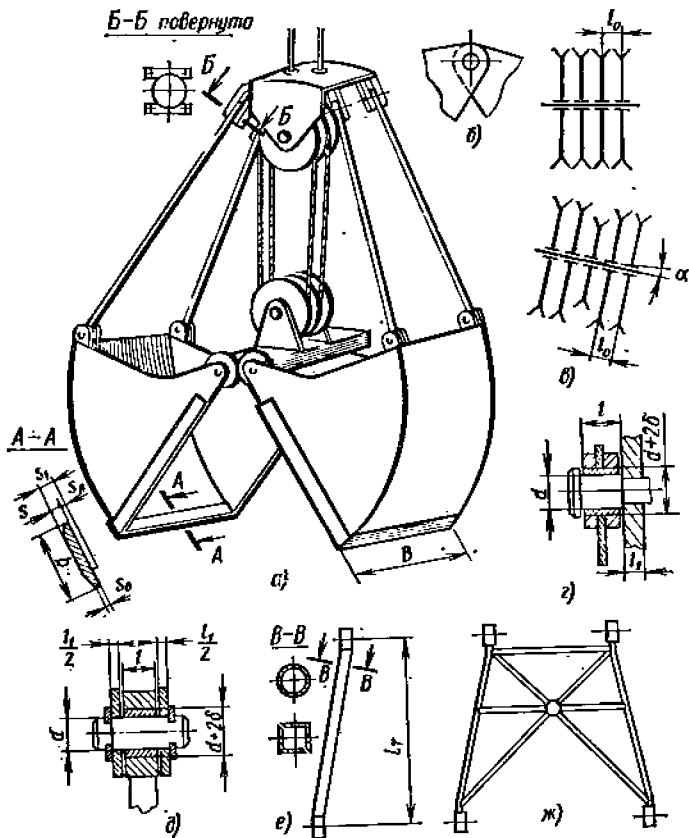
Схема двухчелюстного грейфера: а — общий вид при двухшарнирном креплении челюстей; б — одношарнирное крепление челюстей; в — размещение канатных блоков полиспаста в головке и траверсе; г — шарнир челюсти; д — шарнир тяги; е — тяга; ж — комбинированная тяга
